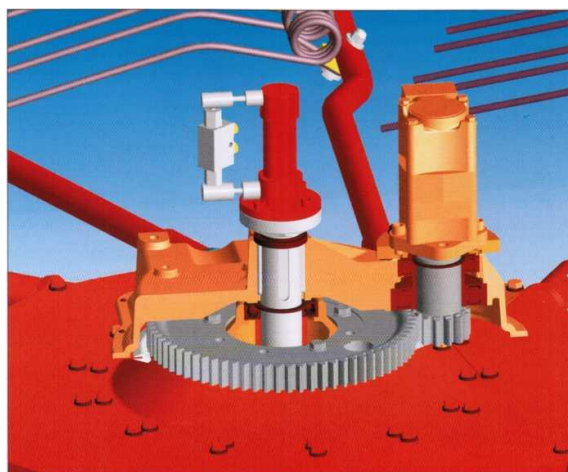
Надежный привод с большими прямыми зубьями шестерни
